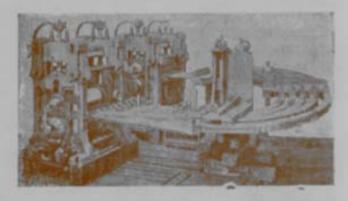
Laminadores del tren acabador con cojinetes de rodillos.
